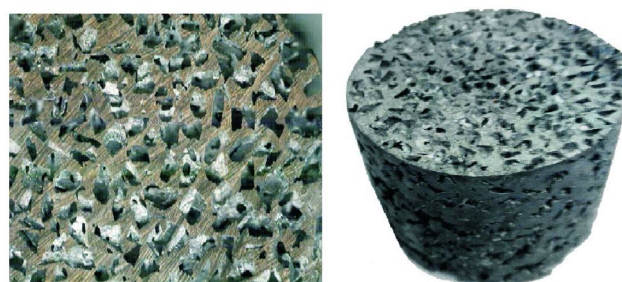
Пористая заготовка — преформа из матричного алюминиевого сплава для ввода в поры частиц малого размера, в том числе и наноразмерных
